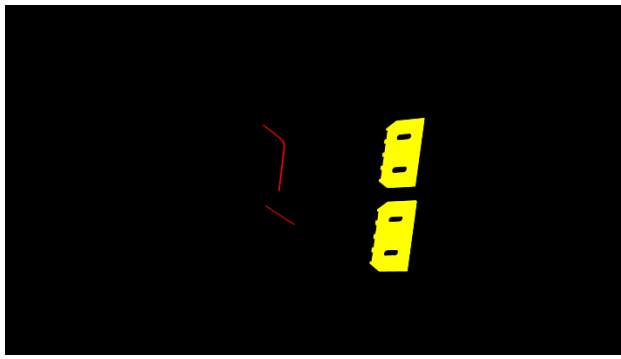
Exemplo de linhas de soldadura.
